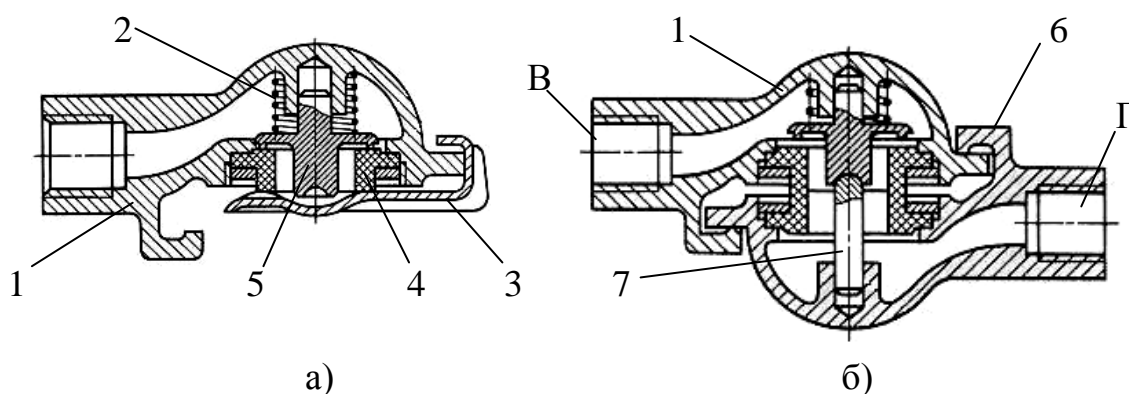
Конструкция узла соединения пневмосистем грузового автомобиля-тягача КАМАЗ и прицепа, связанных по однопроводной схеме: а – соединительная головка «типа А», б – соединение головки «типа А» с головкой «типа Б»; 1 – корпус головки «типа А»; 2 – пружина; 3 – крышка; 4 – седло клапана; 5 – клапан; 6 – корпус головки «типа Б»; 7 – штифт; В – вывод в пневмосистему тягача; Г – вывод в пневмосистему прицепа
